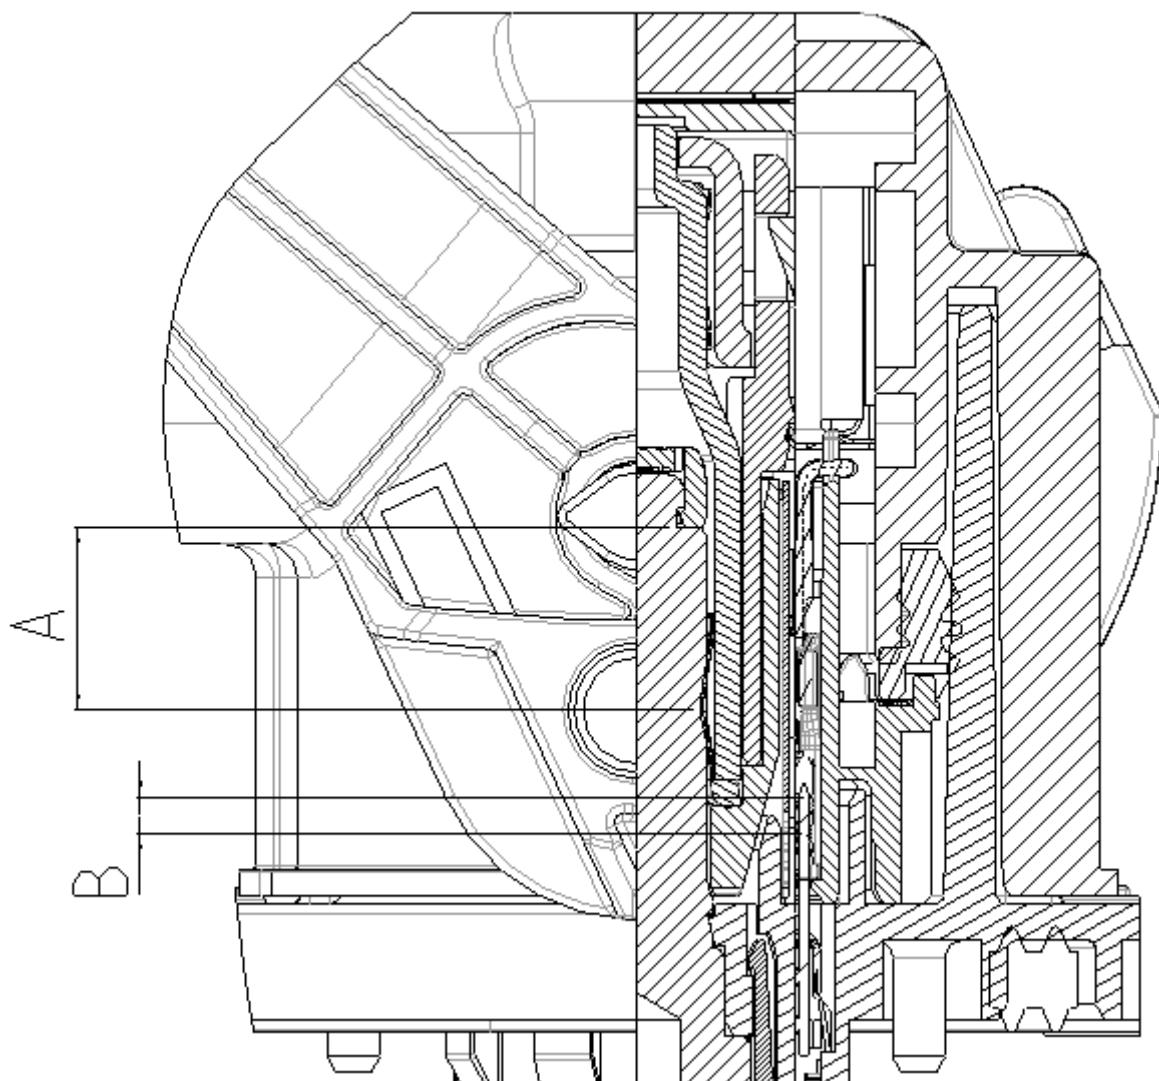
Vibrationsvorrichtung (exemplarische Darstellung mit 2 pol. Stecker)
